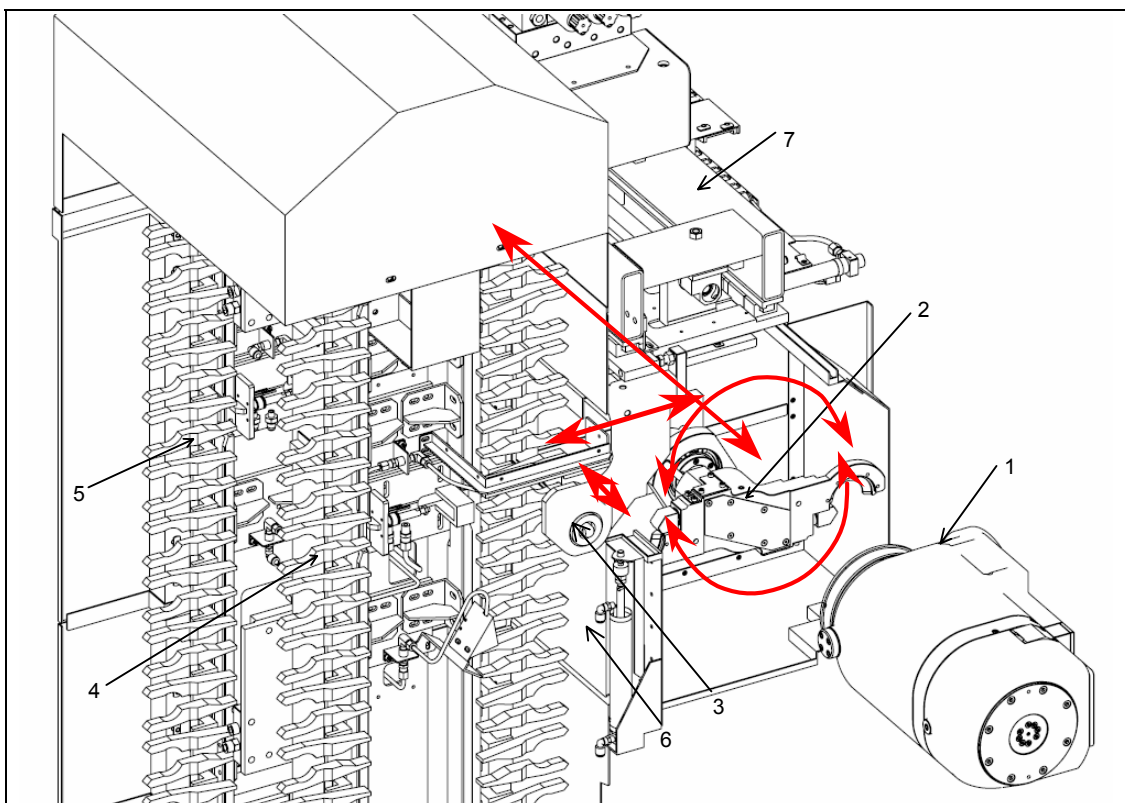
Механизм устройства АСИ (магазин на 72 инструмента)
